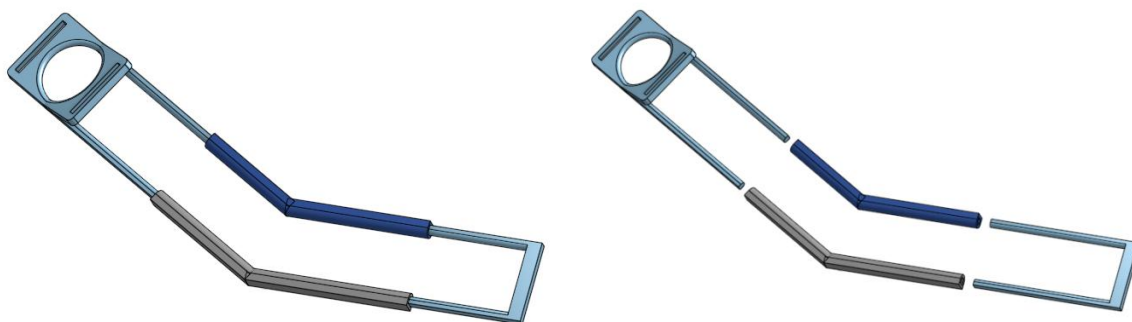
Modèle 3D de la pièce principale du second prototype d'attelle de patte avec une vue assemblée (à gauche) et une vue éclatée (à droite).
